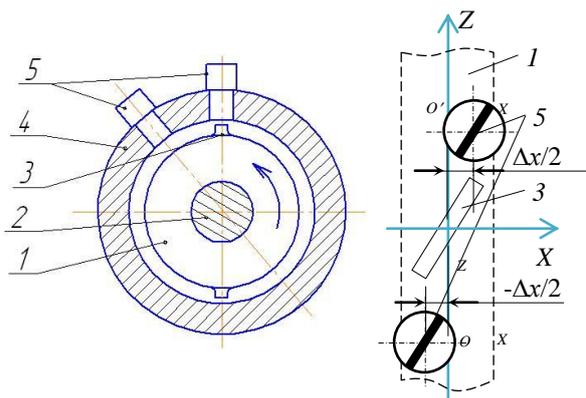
Размещение ОВТД на статоре силовой установки для измерения осевого смещения вала: 1 – колесо; 2 – вал; 3 – лопатка; 4 – статор; 5 – ОВТД
